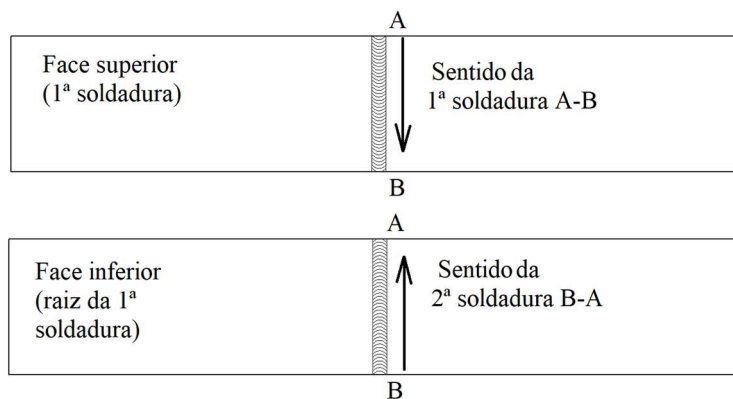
Sentido dos cordões de soldadura para a soldadura pelos dois lados
